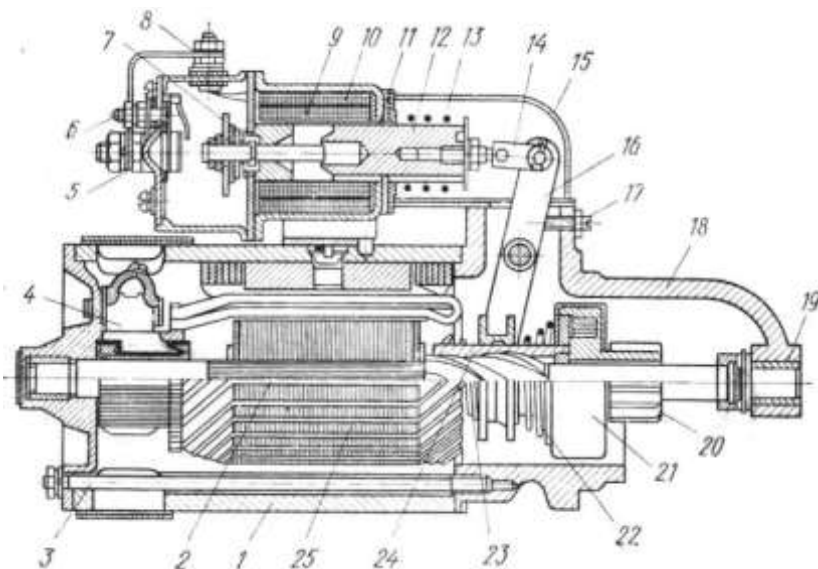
Стартер СТ130-Б: 1 — корпус, 2 — вал якоря, 3 — соединительный болт, 4 — щетка, 5 — главный зажим, 6 — зажим КЗ, 7 — подвижный контакт, 8 — зажим обмоток, 9 — втягивающая обмотка, 10 — удерживающая обмотка, 11 — сердечник, 12 — якорь реле, 13 — пружина якоря, 14 — соединительное звено, 15 — крышка реле, 16 — рычаг приводного механизма, 17 — регулировочный винт, 18 — корпус приводного механизма, 19 — бронзографитовая втулка, 20 — приводная шестерня, 21 — муфта свободного хода, 22 — пружина отводки, 23 — вспомогательная пружина, 24 — резьбовая втулка, 25 — якорь стартера.
